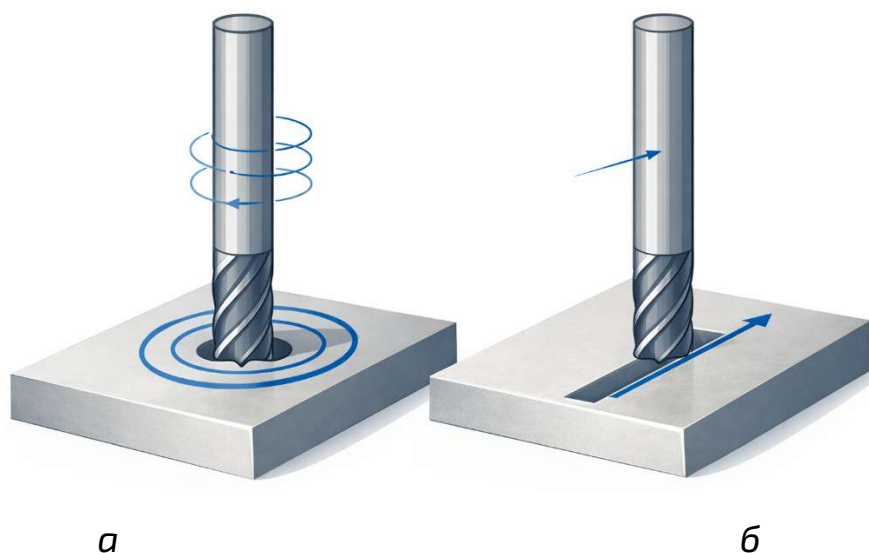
Способи фрезерувань: *а* – спіральне; *б* – прямолінійне
